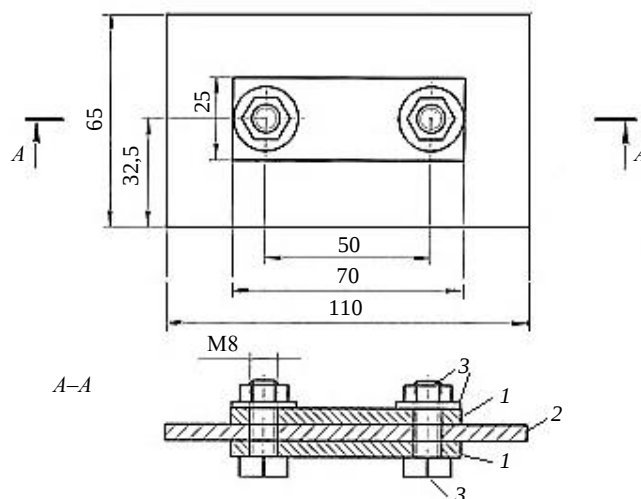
Схема сборки пакета образцов для коррозионных испытаний: 1 – коррозионностойкая сталь с гальваническим покрытием; 2 – алюминиевый сплав с Ан.Окс.нхр; 3 – полипропиленовые болт, гайка и шайба
